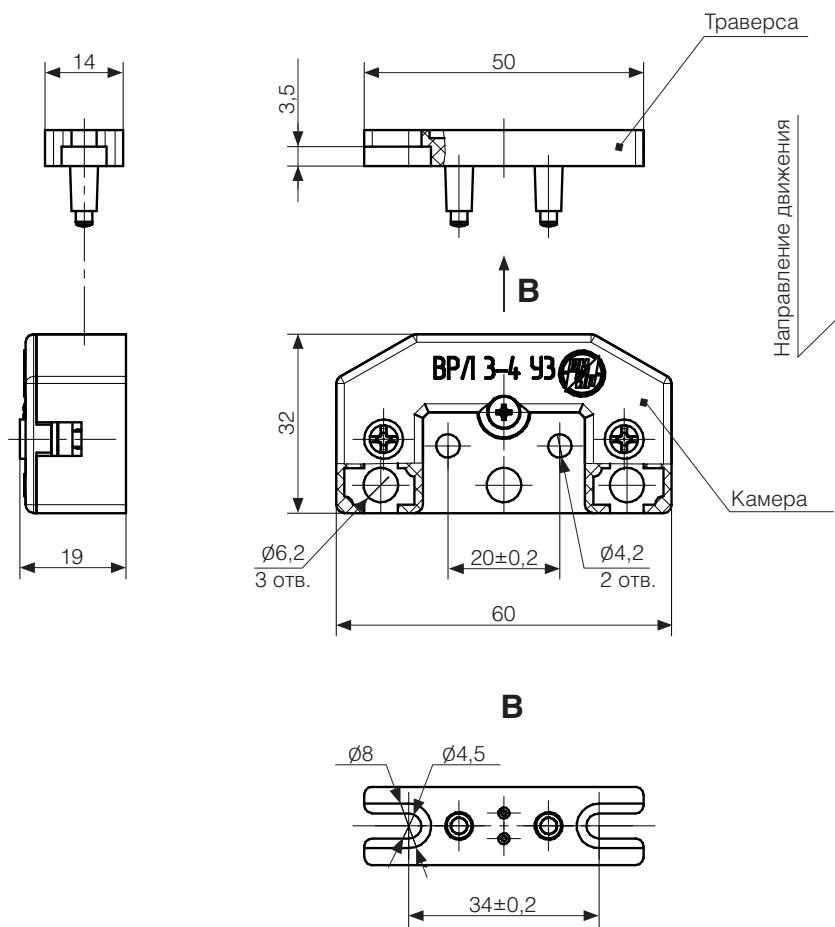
Габаритные, установочные и присоединительные размеры ВРЛ 3-4
